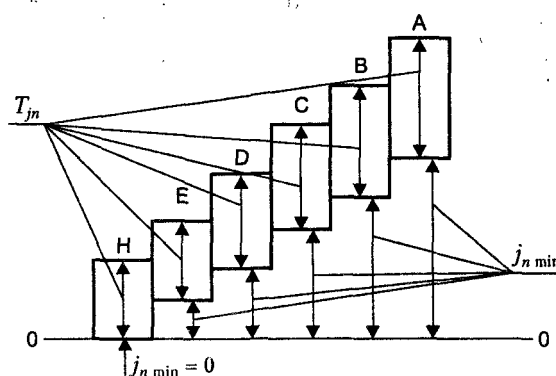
Виды сопряжений и допуски на боковой зазор
